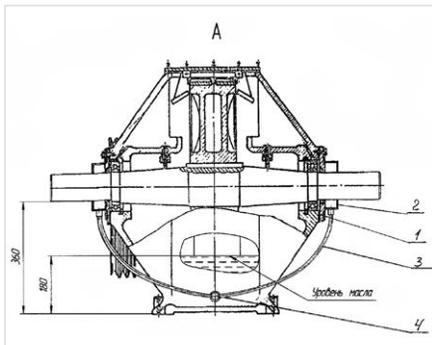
Система сбора утечек масла: 1 — крышка вала; 2 — крышка-емкость; 3 — дренажный шланг; 4 — модифицированная сливная пробка
